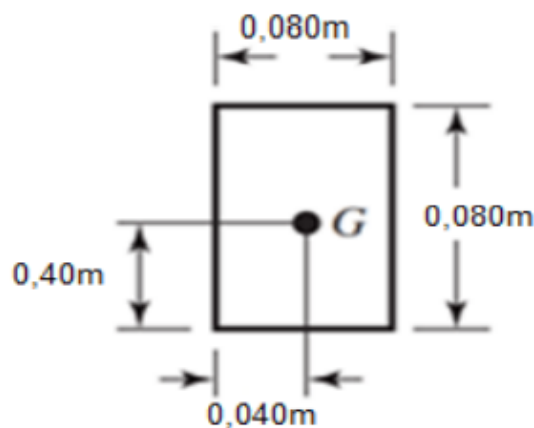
Dimensiones de la junta o cordón de la soldadura. [33]
